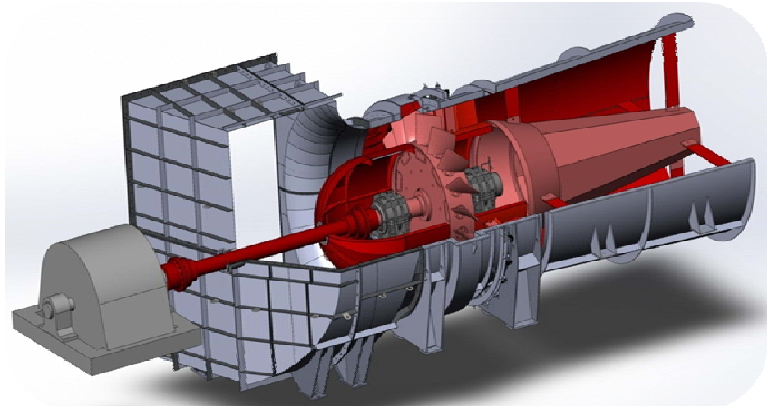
Осевой реверсивный одноступенчатый вентилятор ВО-42,5РЗ нового поколения с противосрывным устройством
